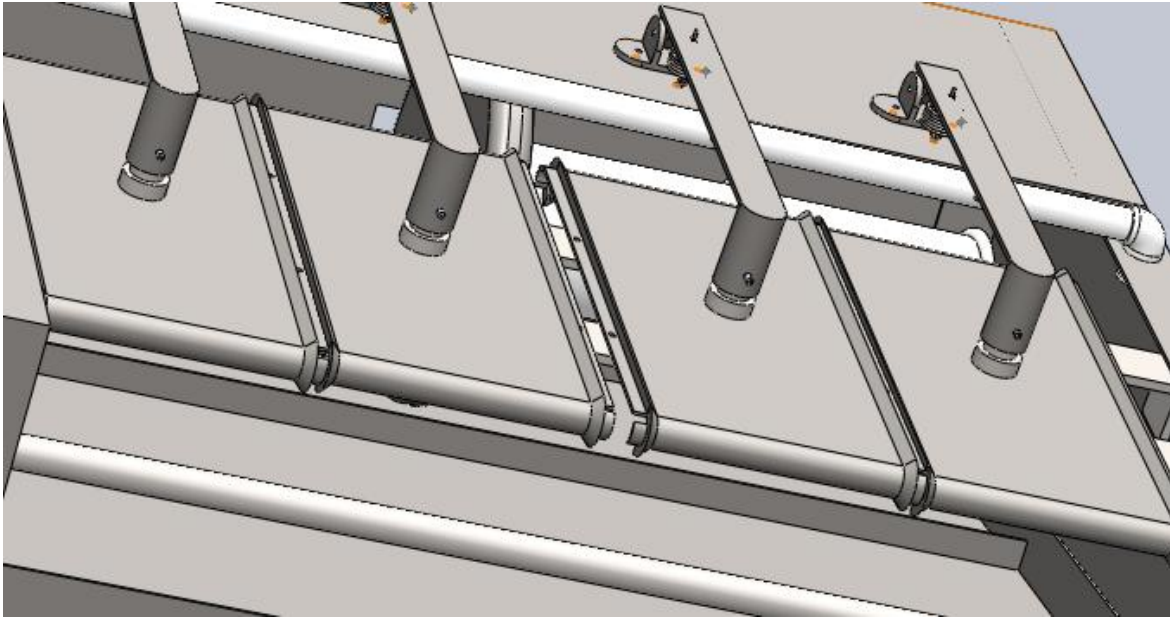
2. Dimensiones que debe poseer soportes según la muestra
